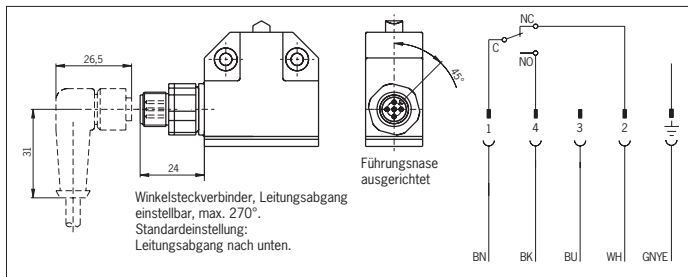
Maßzeichnung/Anschlussplan N01.550SVM5 mit Steckverbinder M12 (SVM5, 5-polig)
